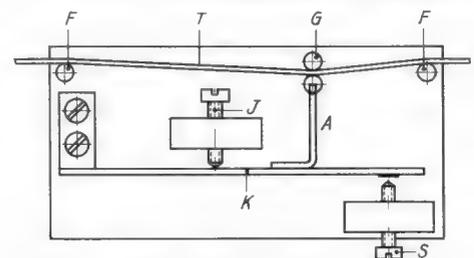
Mechanik des Stoppschalters. A = Kontaktarm; F = Bandführung; G = Gegenlage; J = Justierschraube; K = Kontaktfeder; S = Kontaktschraube; T = Tonband
